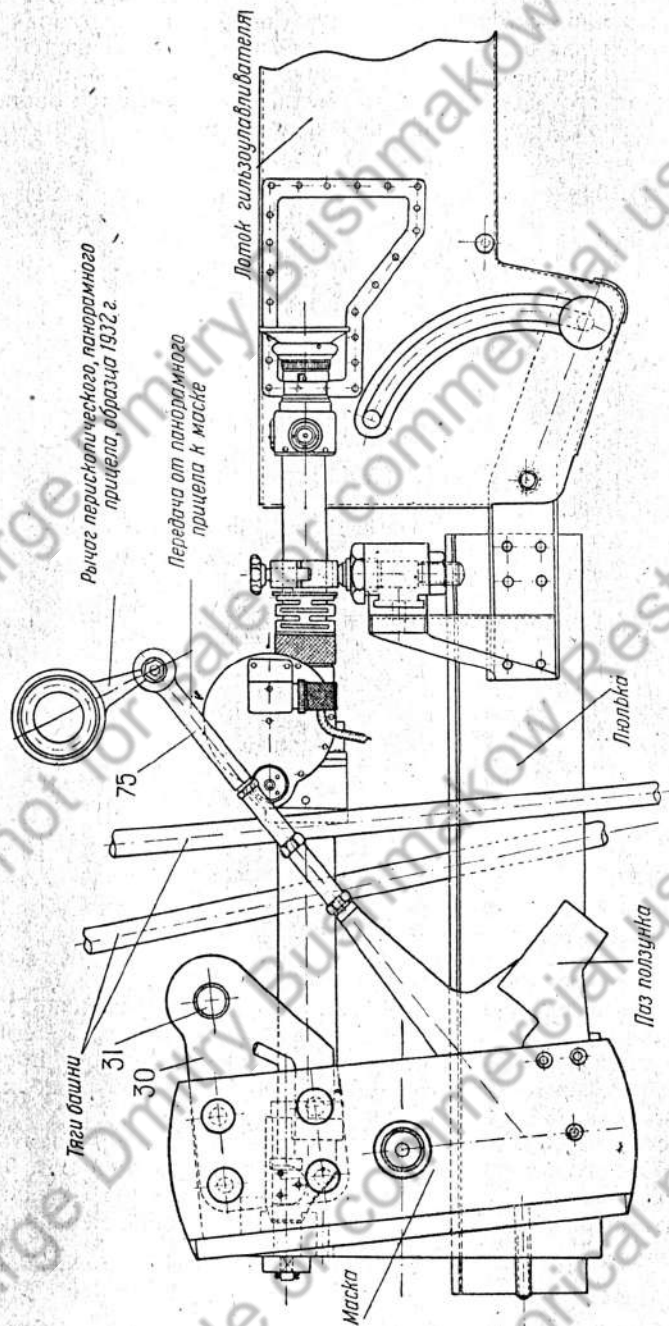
Общий вид размещения привода перископического прицела в танке.
